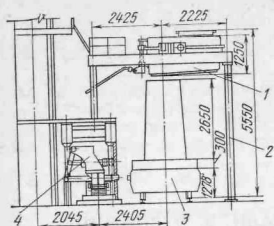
Установка для разливки стали через неподвижный промежуточный ковш: 1 — промежуточный ковш с двумя стопорами; 2 — стенд; 3 — изложница; 4 — толкатель состава
